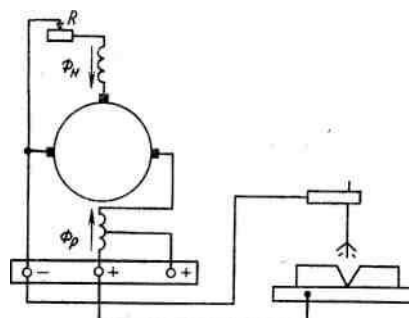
Электрическая схема сварочного преобразователя ПС-500.
